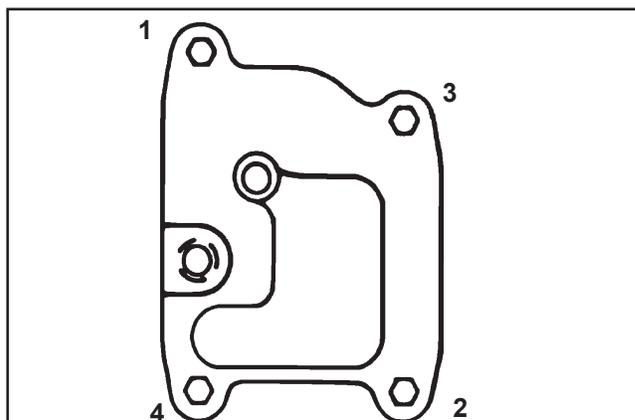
Séquence de couple de serrage du couvercle du reniflard.
